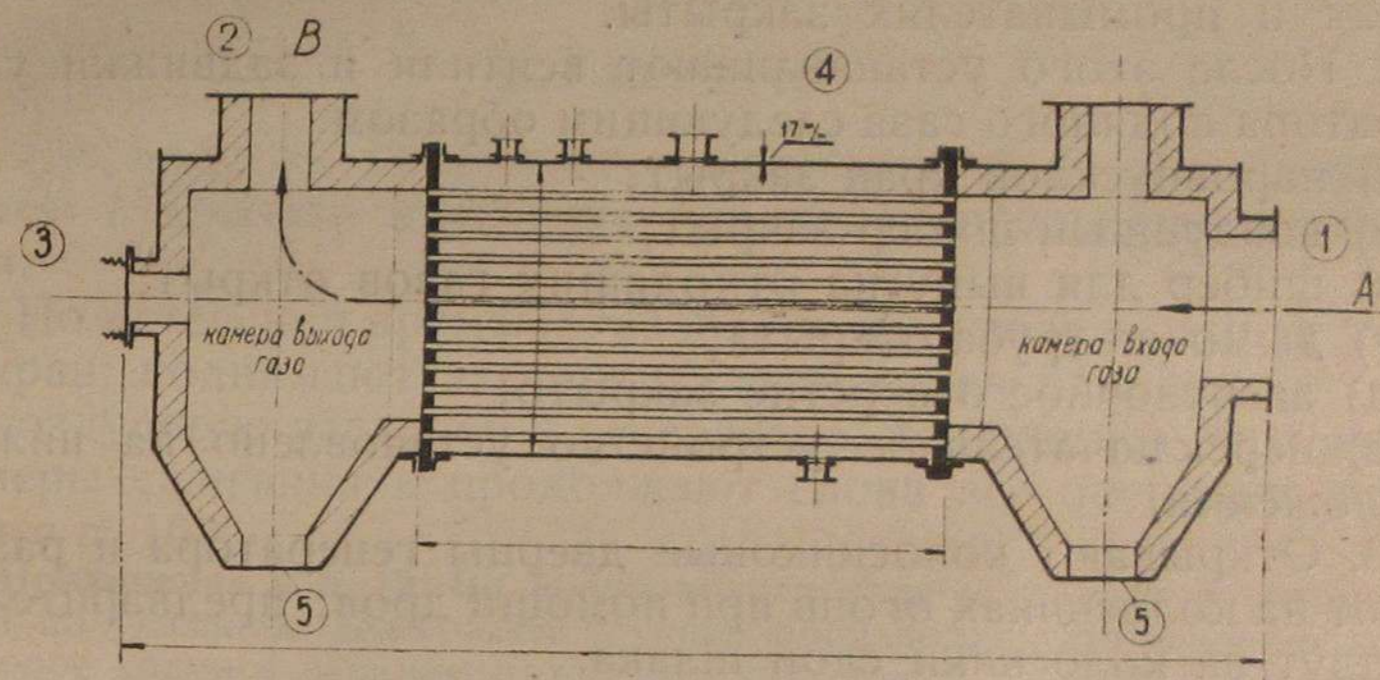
Теплообменный котел Пинча: 1 — вход газа; 2 — выход газа; 3 — взрывной предохранительный клапан; 4 — бочка котла; 5 — зольник.
